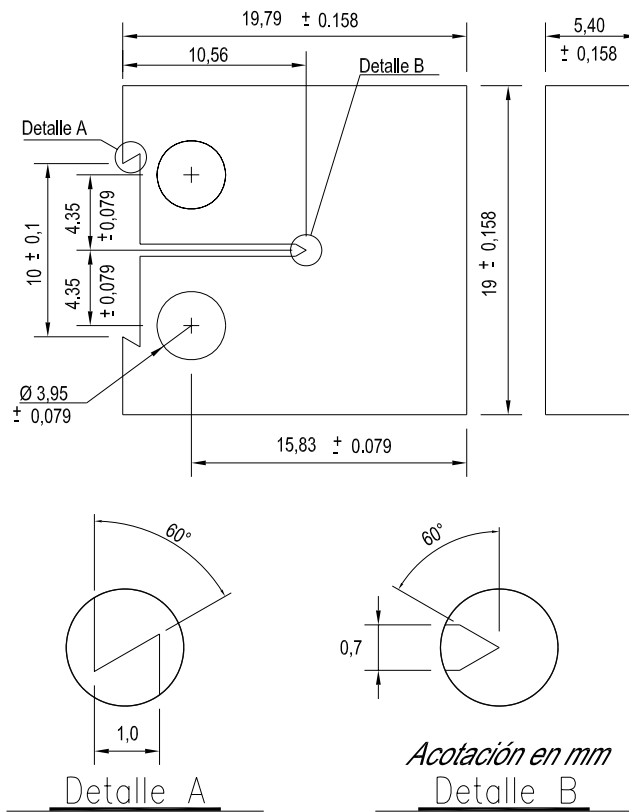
Dimensiones de la probeta compacta de tensión miniatura
